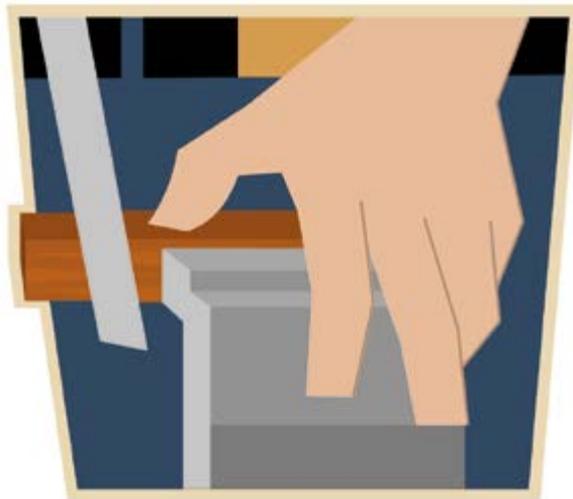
Realización de ranura para iniciar el corte con la segueta de mecánico
